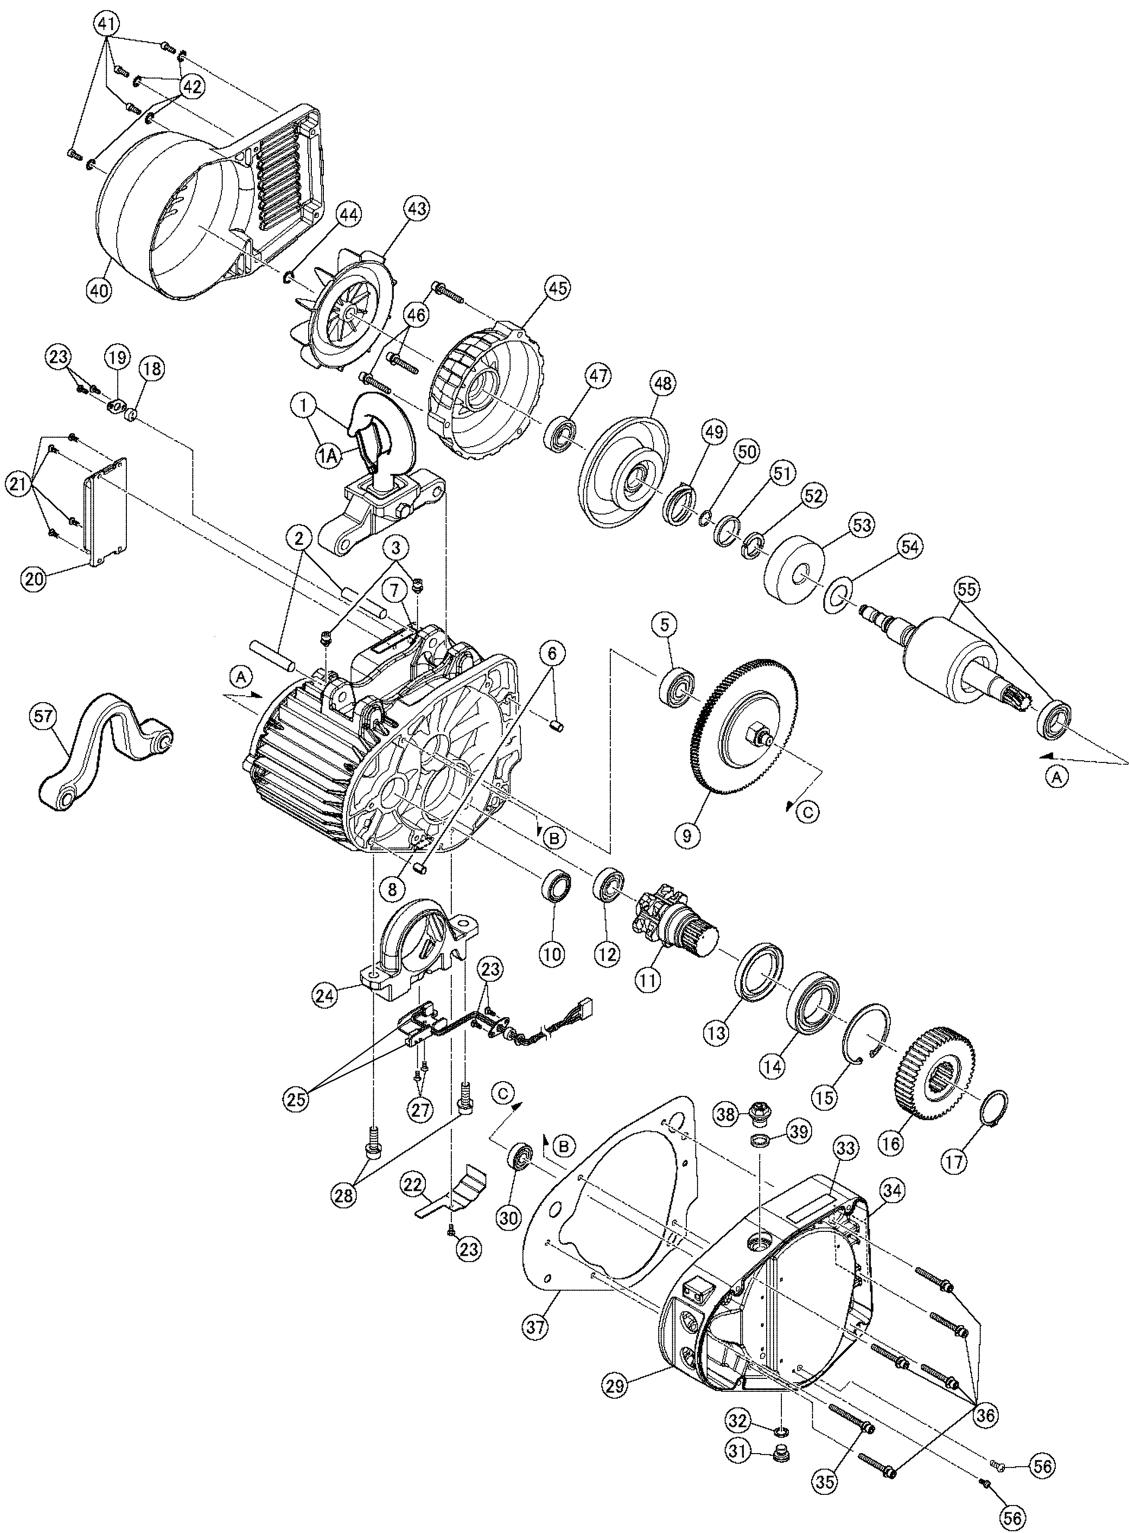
partes de la carcasa, de los engranajes y del motor
